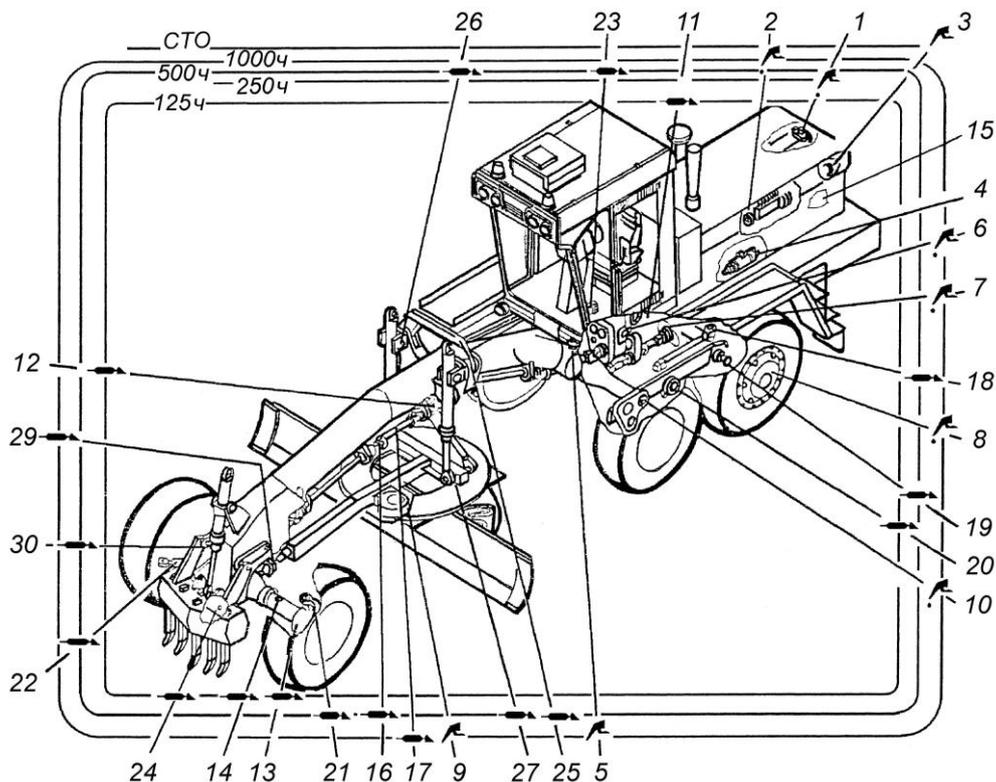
Схема смазки автогрейдера ДЗ-98В: 1 – двигатель; 2 – топливный насос; 3 – натяжное устройство вентилятора (масло М-8Г2к); 4 – стартер; 5 – бак гидросистемы (М-8В2); 6 – блок трансмиссии; 7 – картеры главных передач; 8 – картеры бортовых редукторов; 9 – картер редуктора поворота отвала (все – ТСП-10); 10 – картеры тормозов (моторное масло); 11 – выжимной подшипник муфты сцепления; 12 – подшипники промежуточных опор привода переднего моста; 13 – подшипники поворотных кронштейнов переднего моста; 14 – подшипники опор полуосей переднего моста; 15 – подшипник передней опоры двигателя (все – Литол-24); 16 – подшипники крестовин карданных передач (158); 17 – полости и шлицы карданных валов (УССА); 18 – шаровые пальцы реактивных штанг; 19 – шаровые опоры подвески задних мостов; 20 – подшипники оси балансиров; 21 – шаровые пальцы поперечной тяги управления; 22 – шаровые пальцы гидроцилиндра рулевого управления; 23 – оси привода муфты сцепления, рычагов управления блокировки; 24 – подшипники подвески переднего моста; 25 – подвеска тяговой рамы; 26 – цапфы гидроцилиндров подъема и выноса тяговой рамы; 27 – подшипники подъема и выноса тяговой рамы и выдвигания отвала; 28 – подшипники штоков гидроцилиндров поворота отвала и изменения угла резания; 29 – шкворень тяговой рамы; 30 – шарнирные соединения дополнительного рабочего оборудования (все – Пресс-солидол С)
